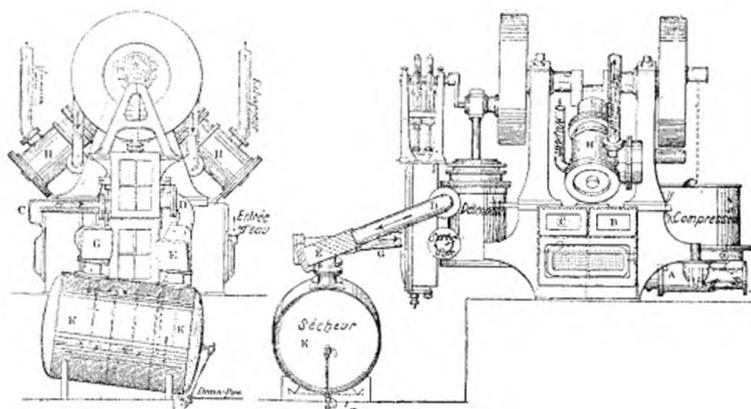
et 46. — Hall. Machines à cylindres inclinés
